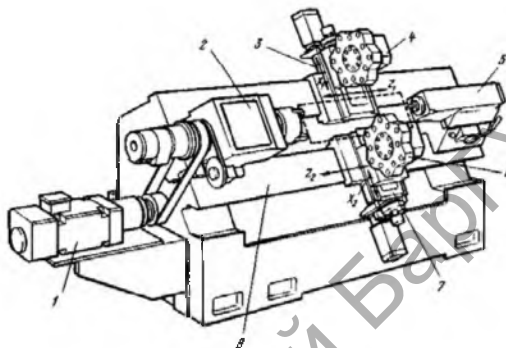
Наклонная компоновка токарного станка с ЧПУ
